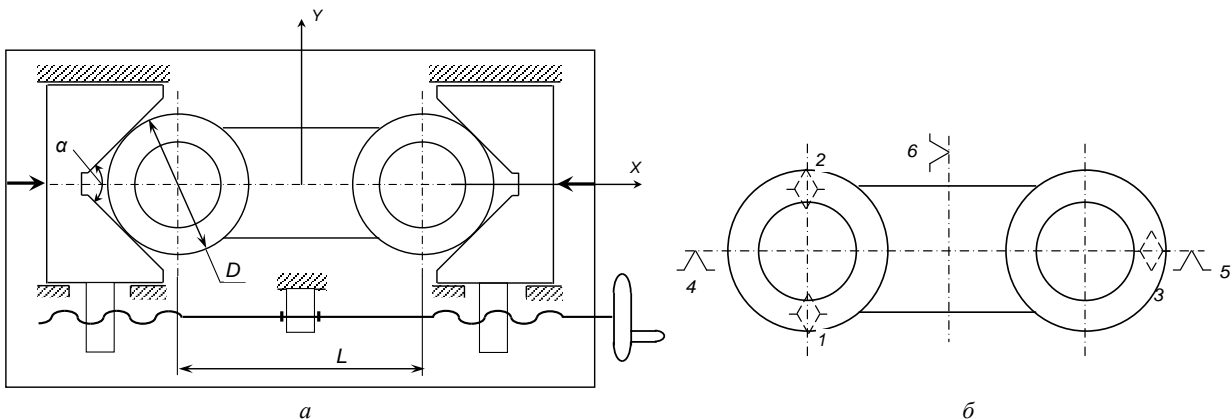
Конструктивна схема верстатного пристрою, що реалізує установа заготовки деталі типу «Важіль» в самоцентрувальні лещата з призматичними губками:
